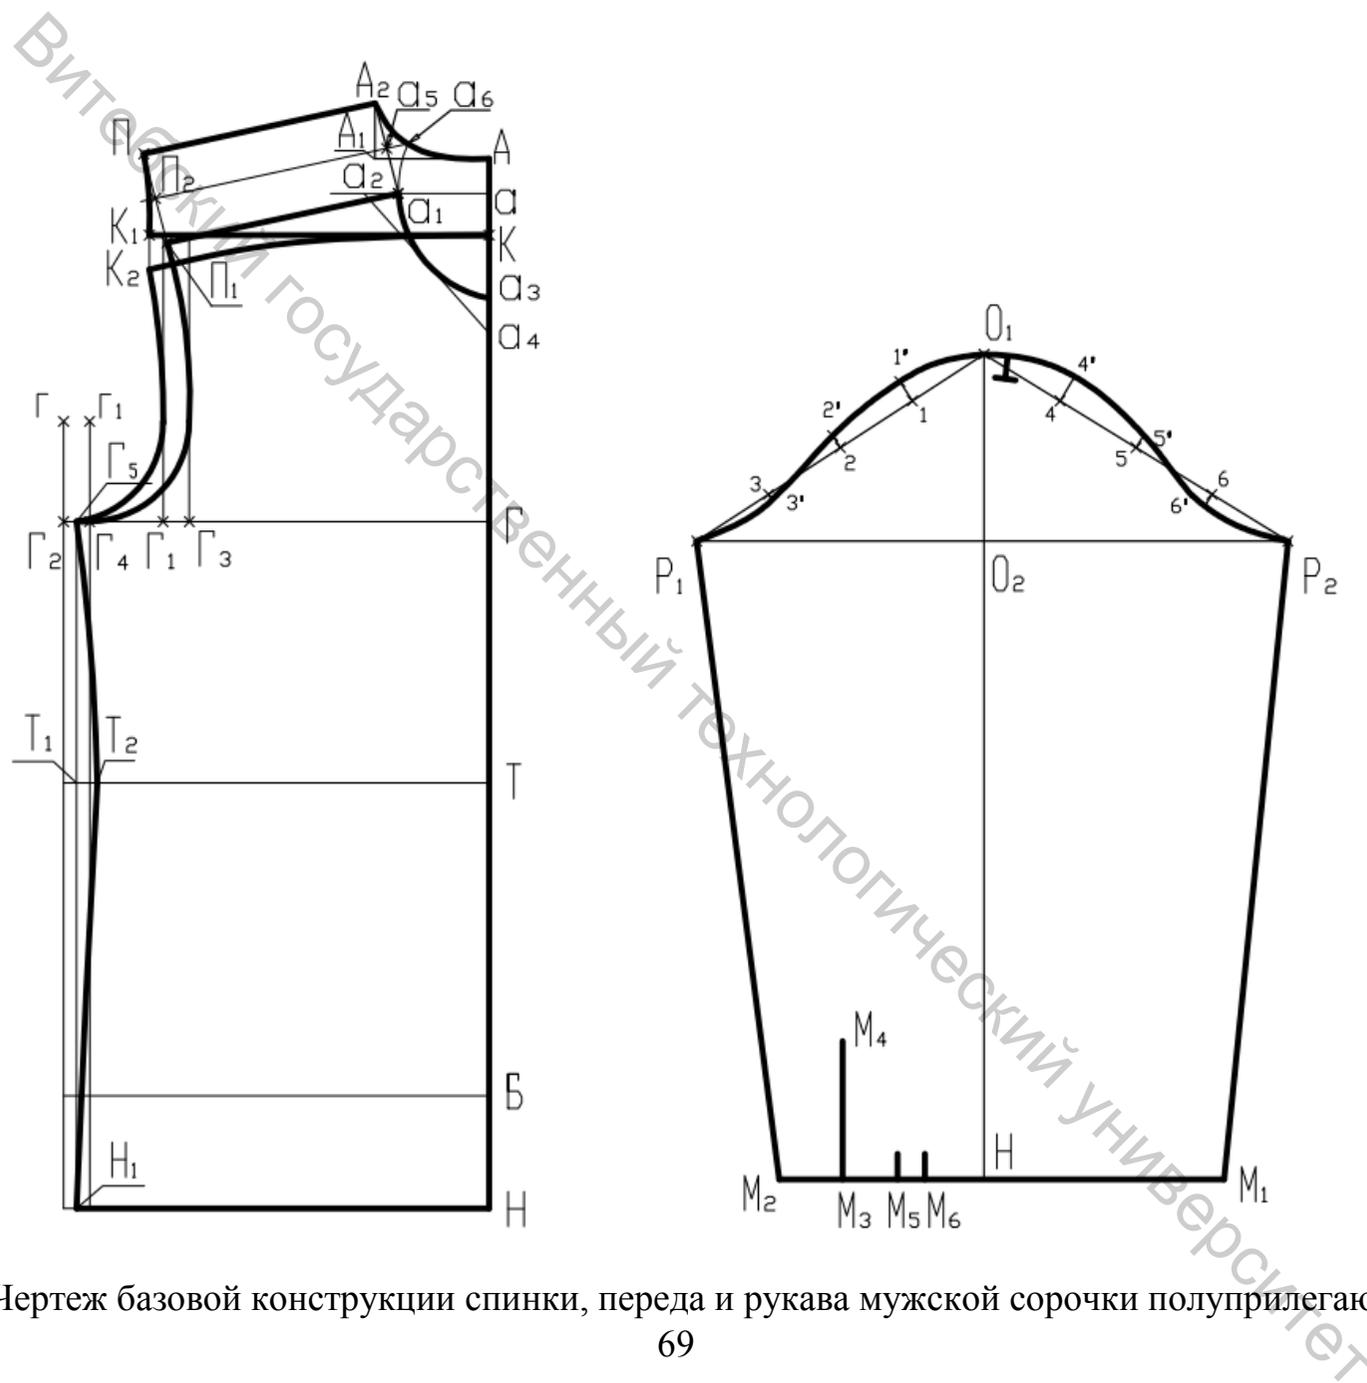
Чертеж базовой конструкции спинки, переда и рукава мужской сорочки полуприлегающего силуэта
